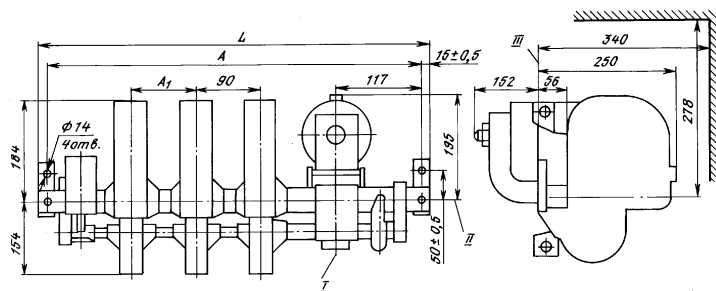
Габаритные и установочные размеры контакторов КТП6042 и КТП6043
